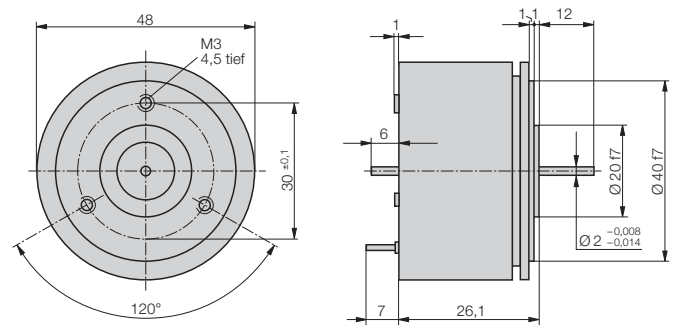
KINAX 3W2 mit Antriebswelle vorn 2 mm Ø, Länge 12 mm, hinten 2 mm Ø, Länge 6 mm.
